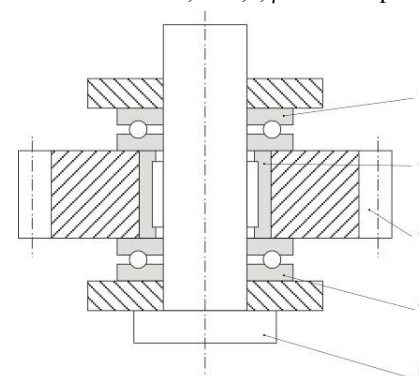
Схема приспособления для обкатки зубчатых колес
